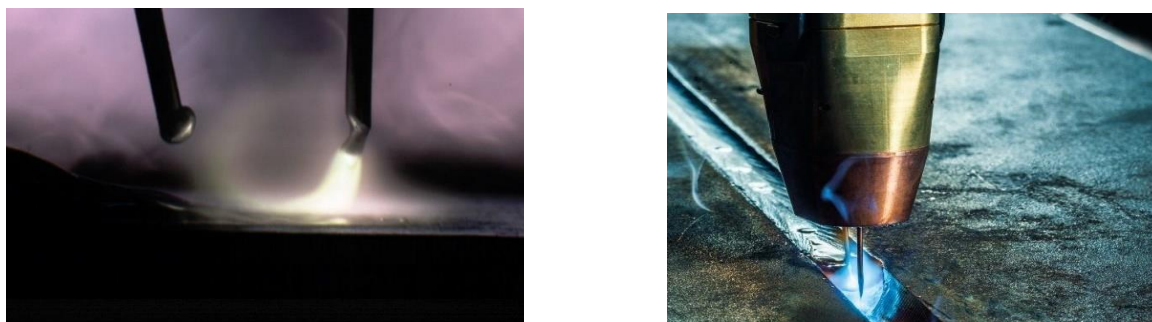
работа сварочной дуги в процессе СМТ Twin
